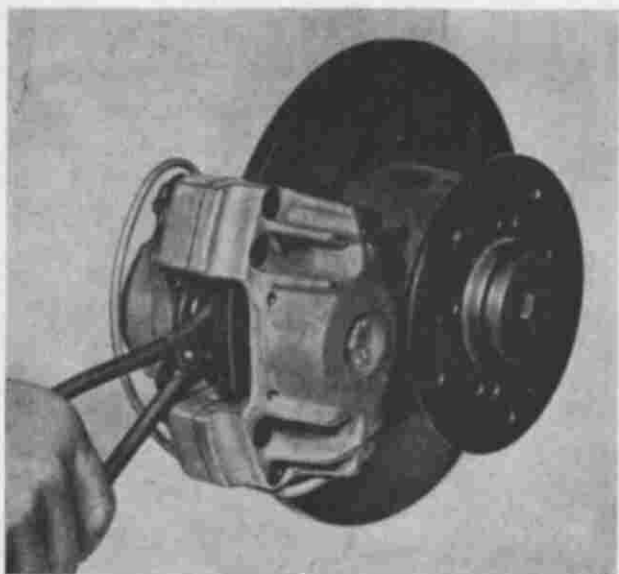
Mit der Kolbendrehzange wird der Kolben in die genaue Lage gemäß der Schräglehre gebracht
